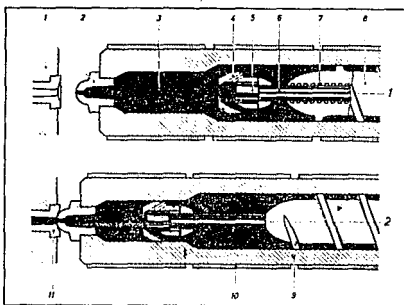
Máquina de inyección por pistón de una etapa [6].
